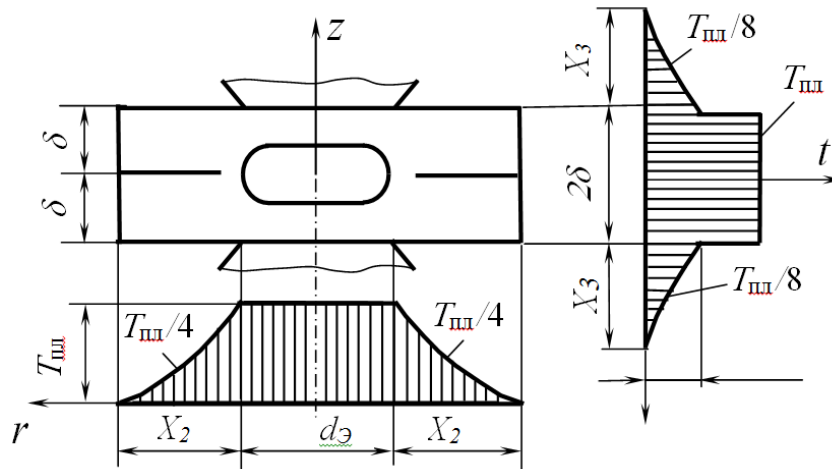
Расчетная схема нагрева металла при точечной сварке
